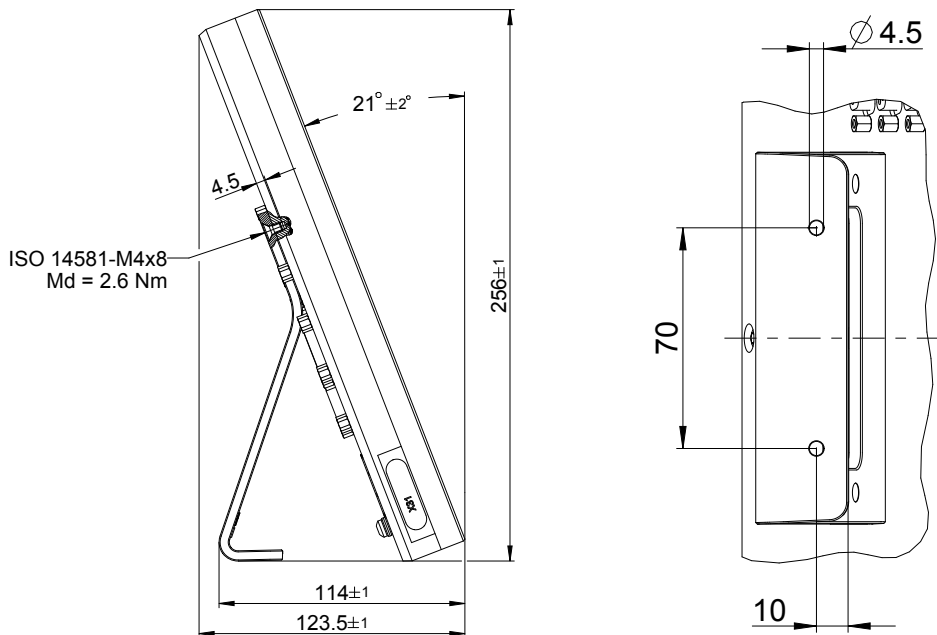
Dimensões do aparelho com pé de suporte Single-Pos
